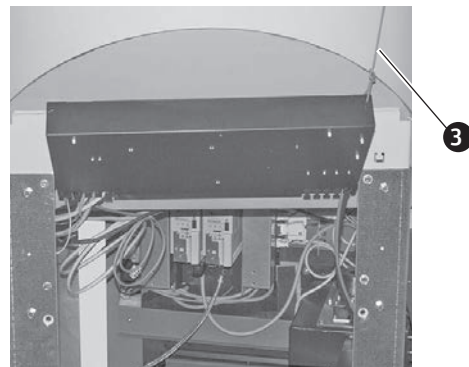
Schaltfeld aufklappen und mit Seil oder Draht fixieren
